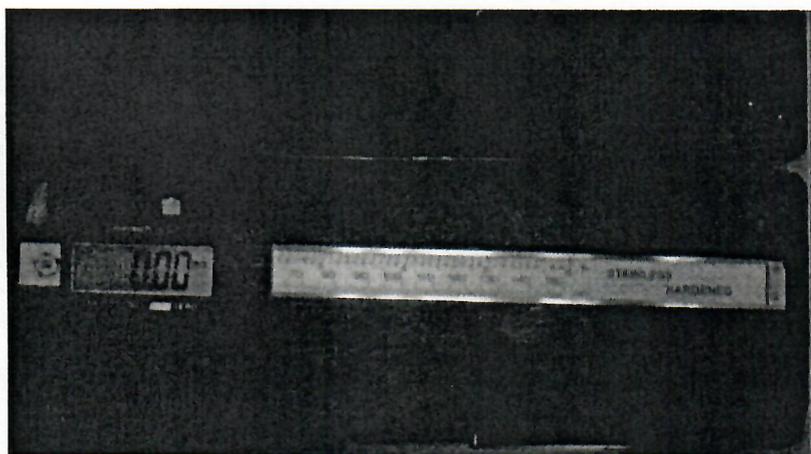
Общий вид штангенциркулей типа ШЦЦ-I.
